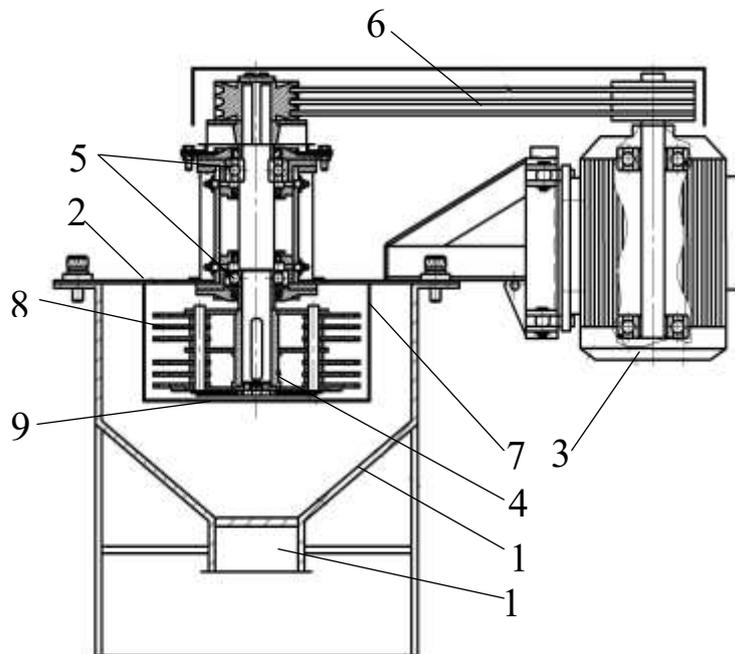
Вертикальные дробилки ВД (конструктивная схема):
